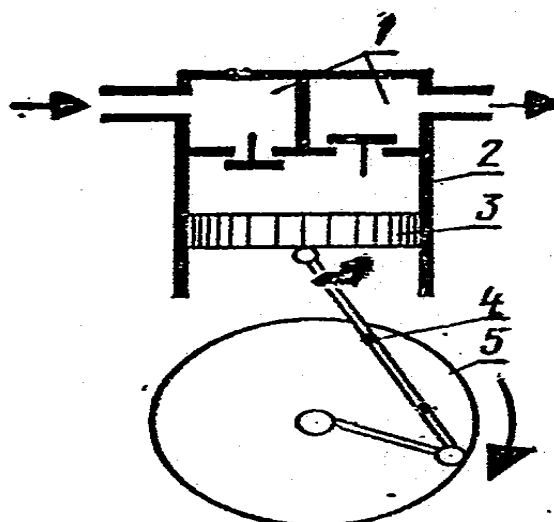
Схема работы поршневого компрессора*: 1 – клапаны, 2 – цилиндр, 3 – поршень, 4 – шатунно-кривошипный механизм, 5 - маховик
